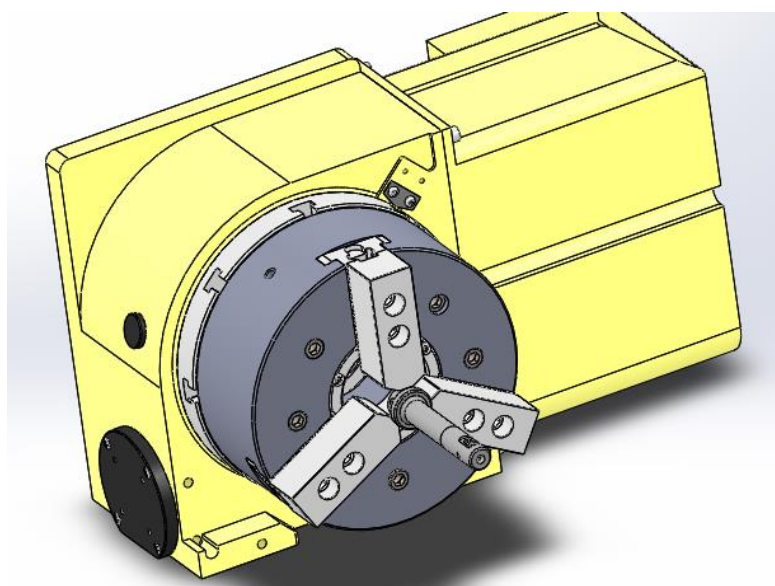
Пристосування для фрезерування пазу для установки твердосплавної пластини
